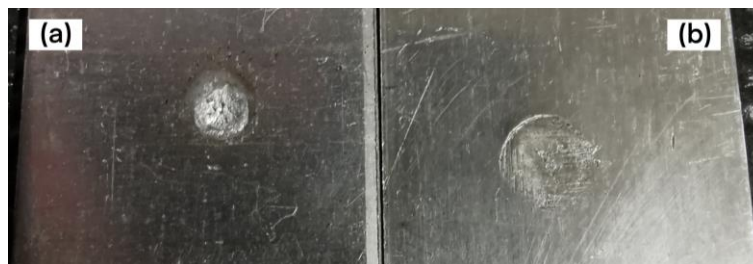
Visualização da zona interna do ponto de soldadura (a) e do entalhe (b) após a quebra da ligação soldada nas chapas de alumínio que sofreram limpeza superficial com acetona
